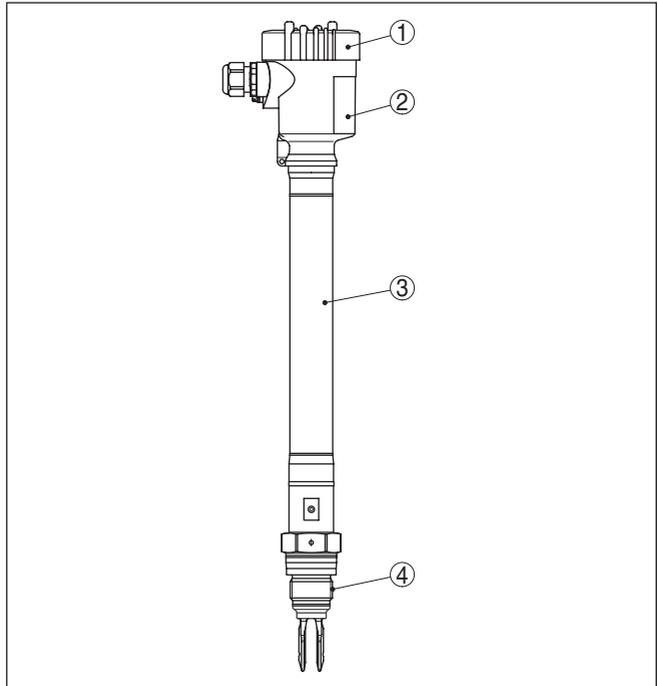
VEGASWING 66, Kompaktausführung mit Kunststoffgehäuse
